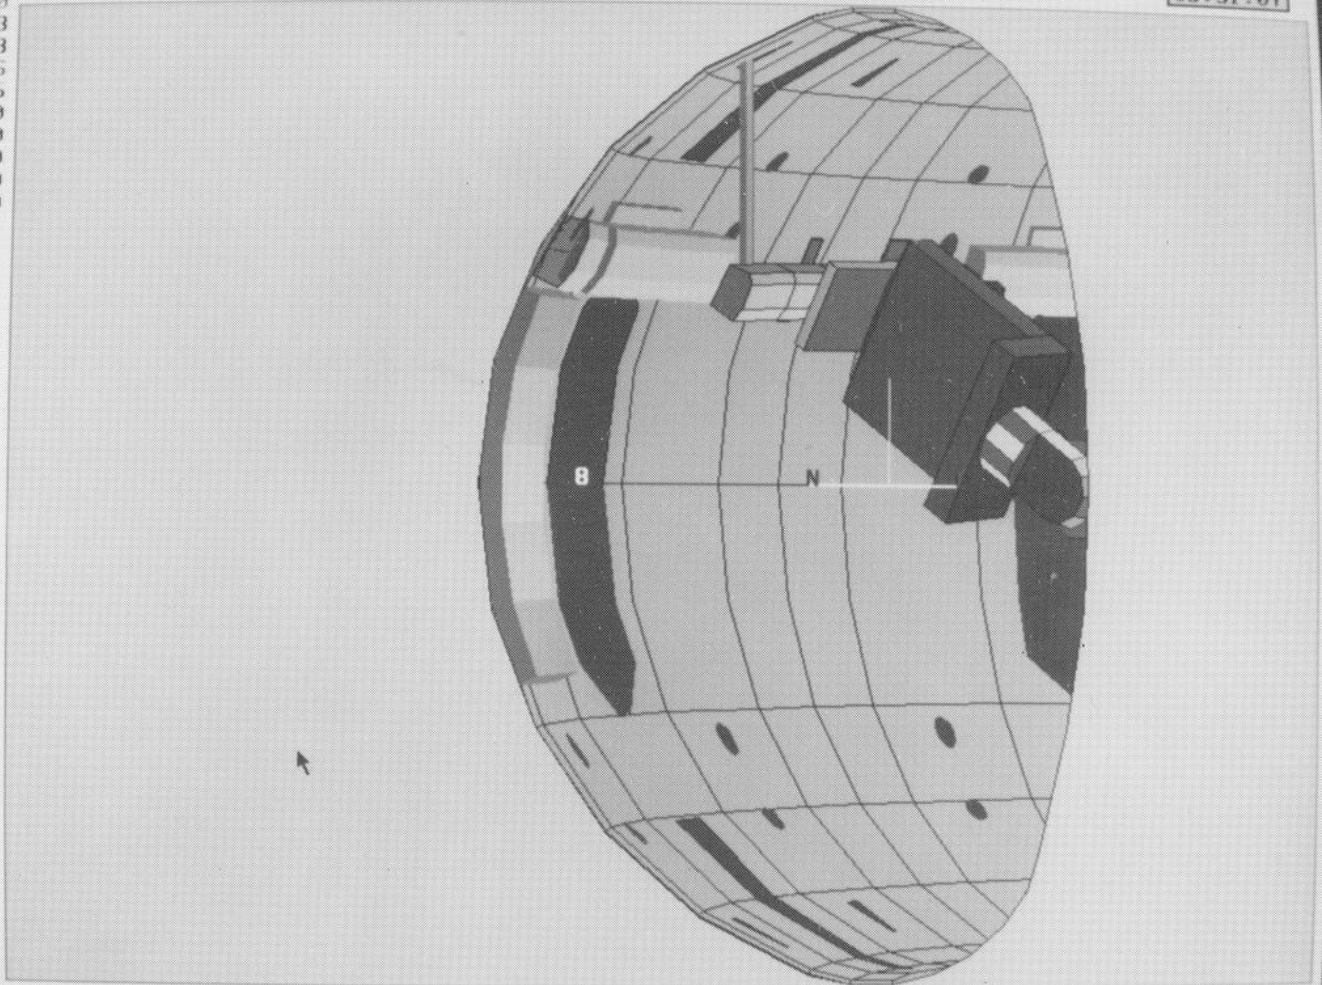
Chariot de soudure TIG se déplaçant sur le guide de soudage
